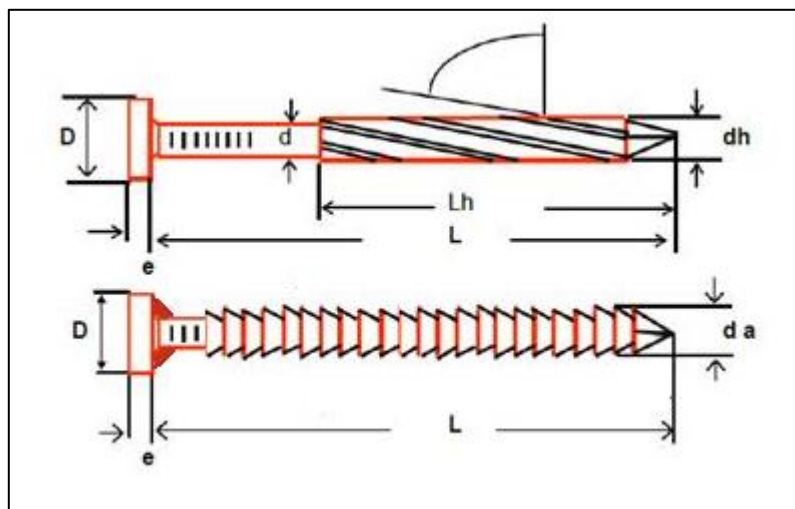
Dimensiones de elementos de unión (cedida por INCHALAM)
